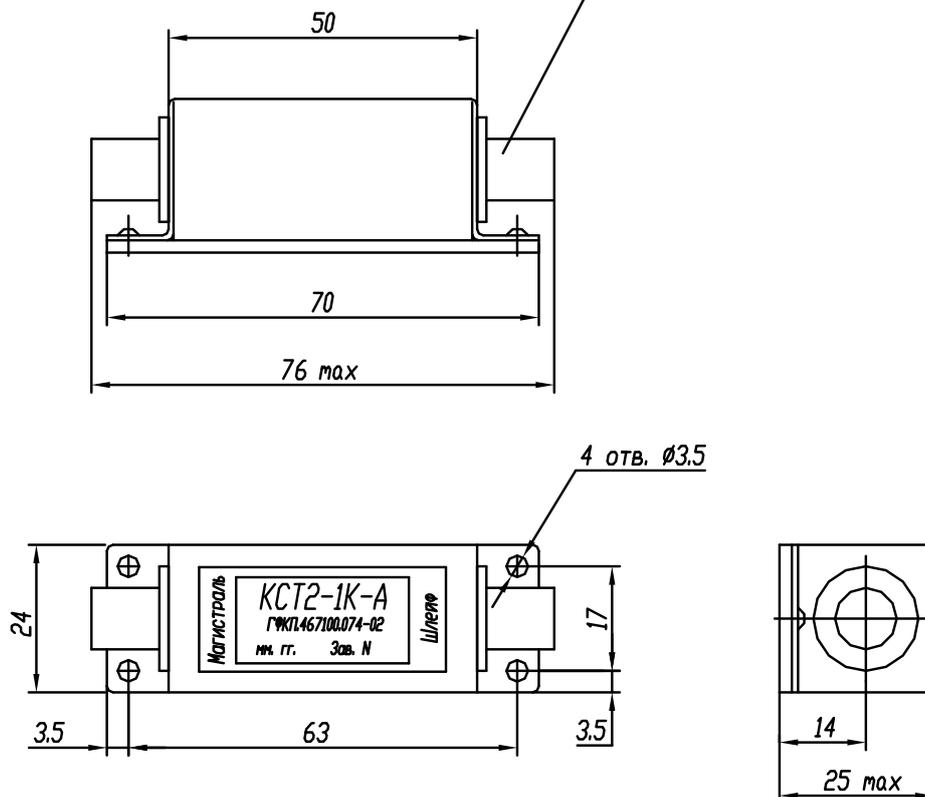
Габаритный чертеж коробки соединительной КСТ2-1К
